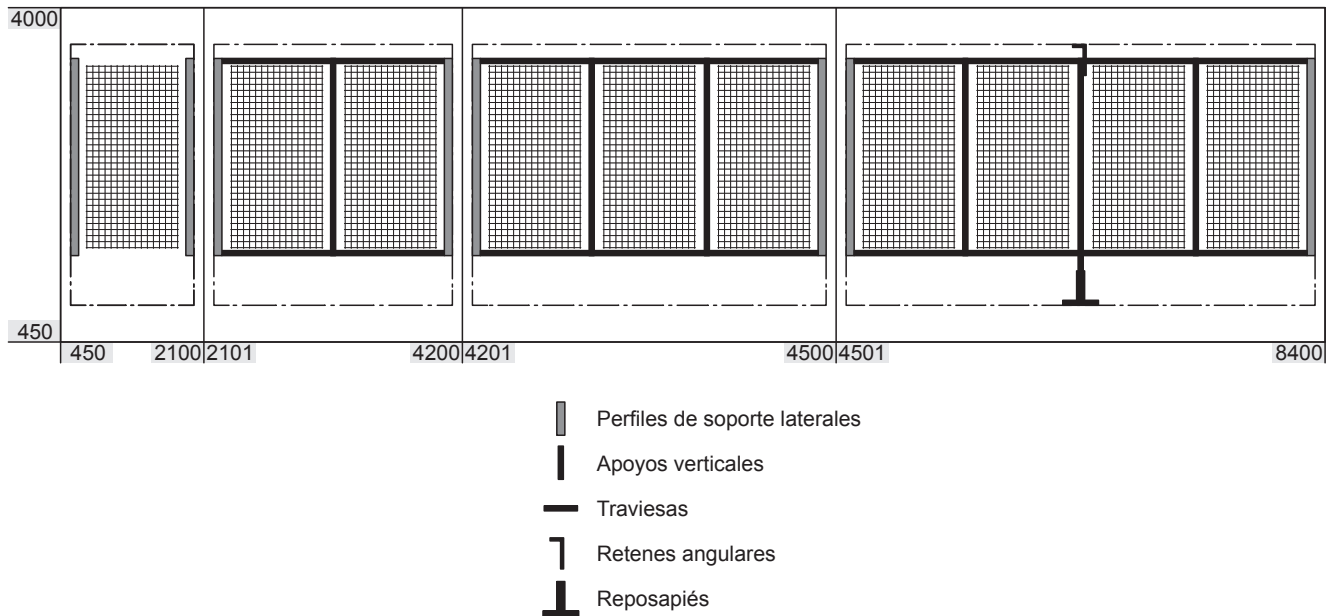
Resumen de las estructuras de bastidor del sistema de boquillas (dimensiones internas del canal en mm)
